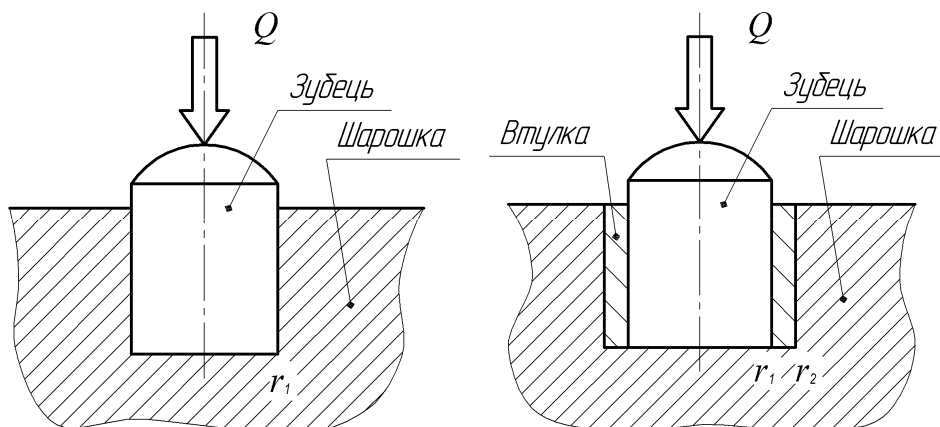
Схеми конструкцій з'єднання зубця з шарошкою
